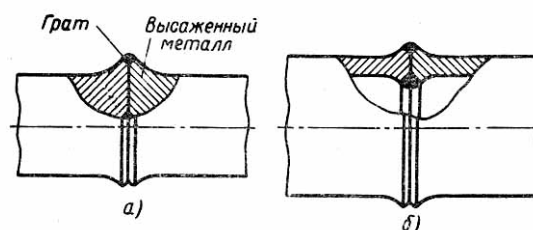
Стыки, сваренные оплавлением а – стержня; б – трубы
